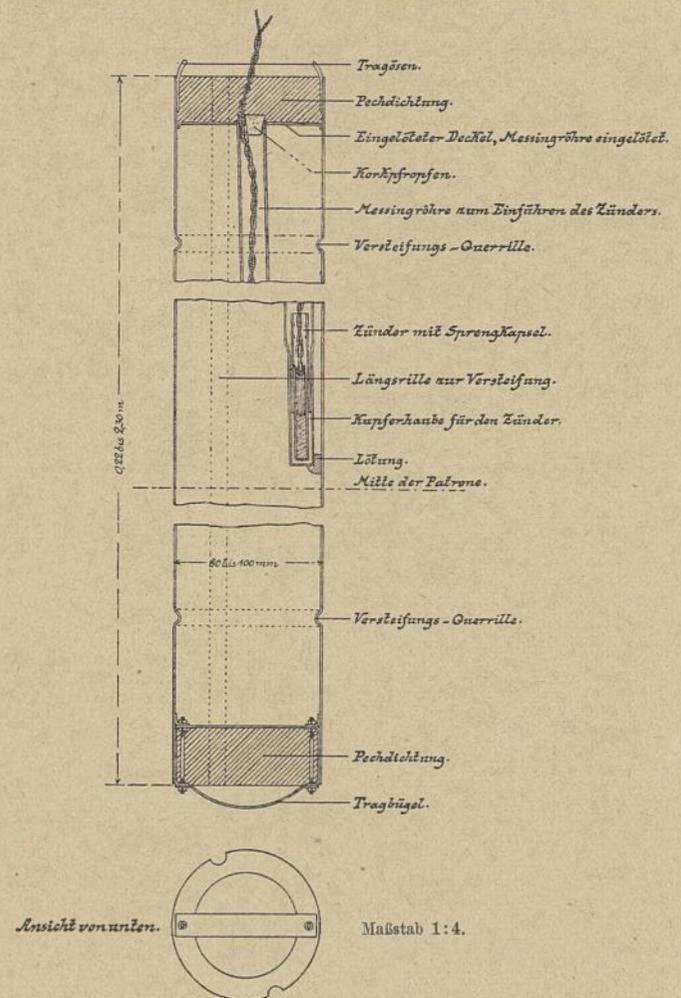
Sprengpatrone für die Bohrlöcher der Kreuzermole.
